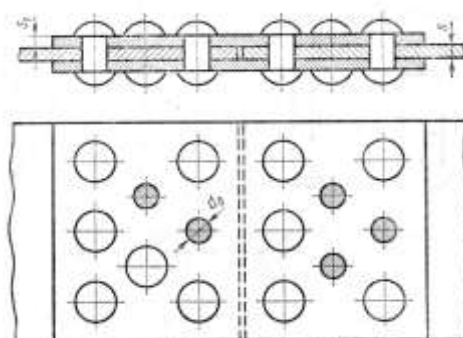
Многорядный двухсрезный шахматный заклепочный шов с двумя накладками
